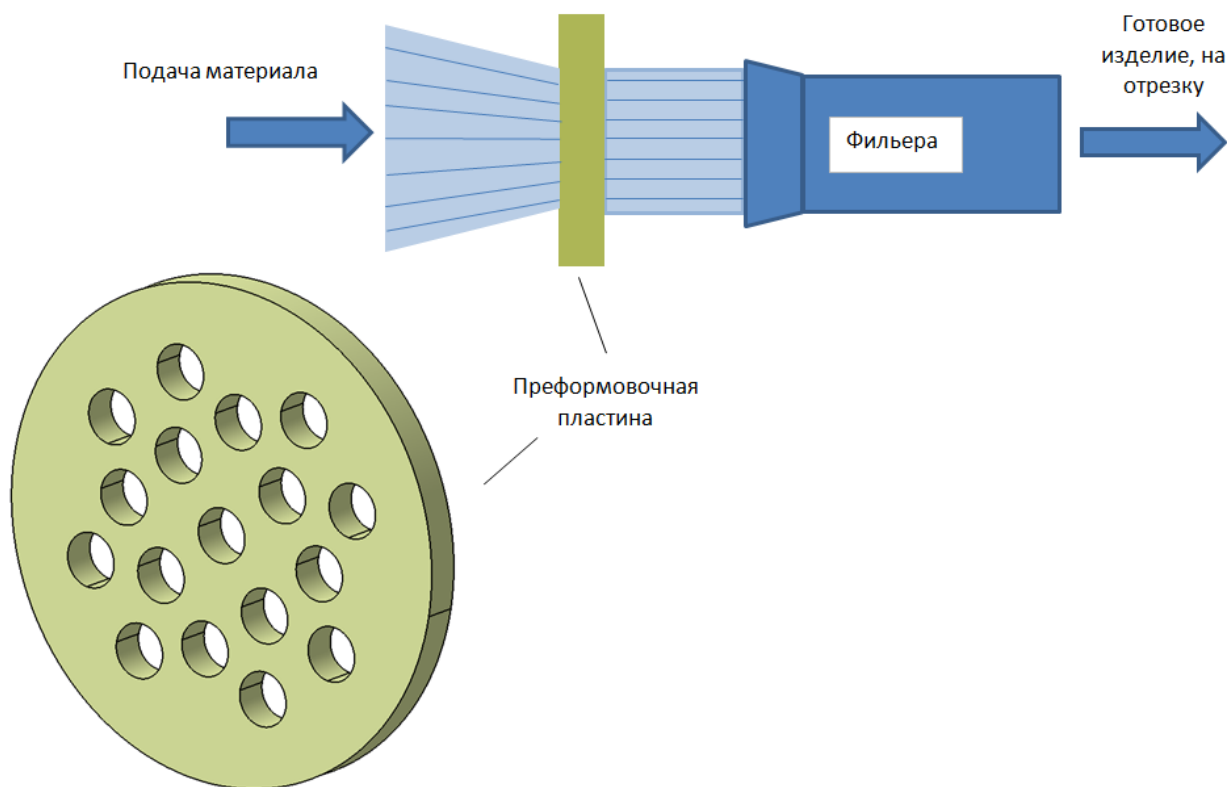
Преформовочная пластина, устанавливаемая перед фильерой для получения равномерного пучка волокон (схематичный вид)
